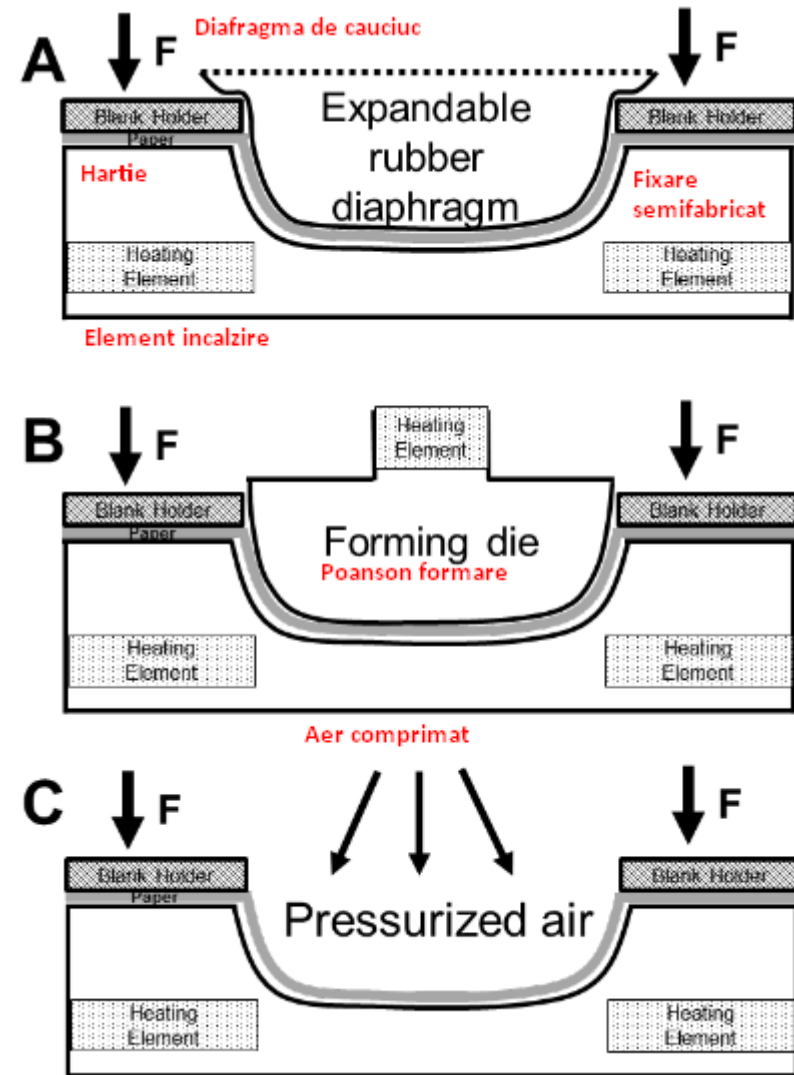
Formare cu fixarea semifabricatului (fixed blank forming processes)
